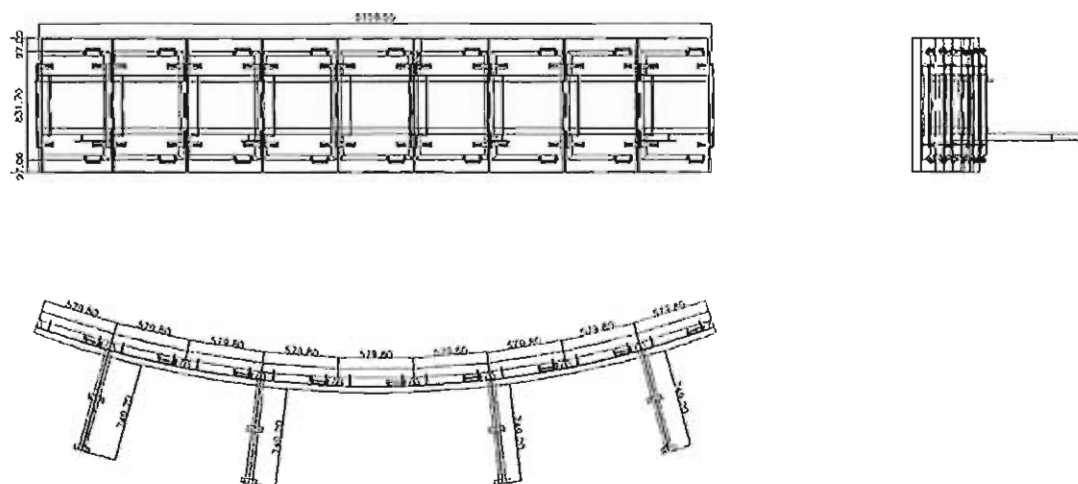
Estudo para a elaboração dos suportes dos painéis de Video Wall no Plenário.
